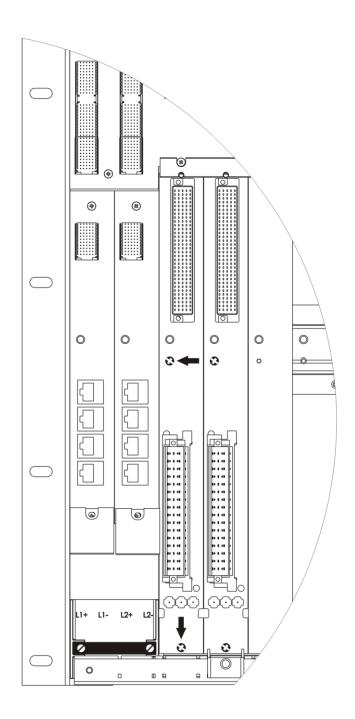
Festschrauben des mono Connector Boards, exemplarisch
